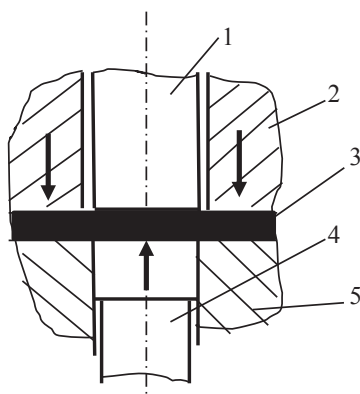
Схема чистовой вырубки (пробивки) с предварительным сжатием заготовки:
